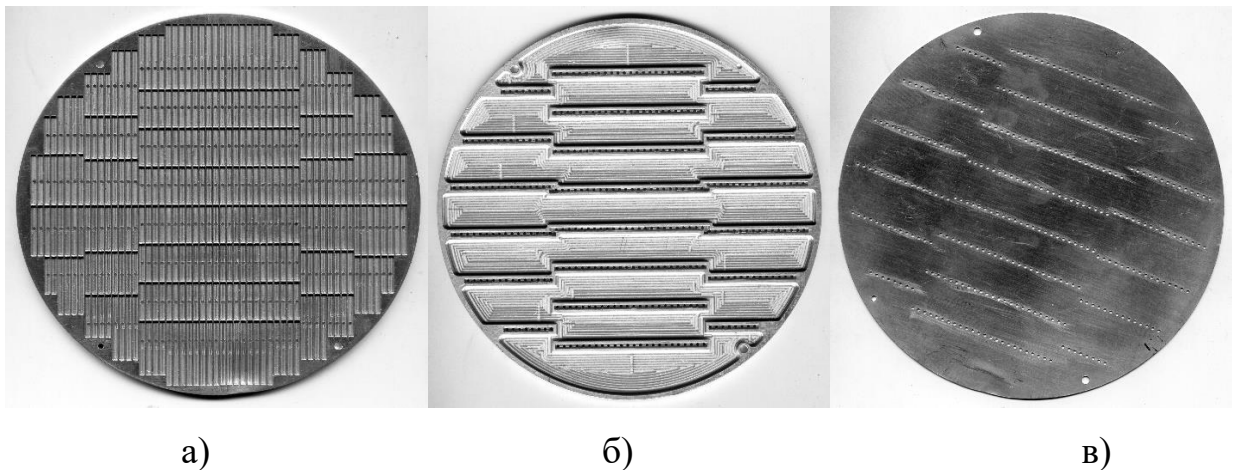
Зовнішній вигляд тонкостінних деталей слотової антени: корпус (а); решітки з прорізами (б), (в)
